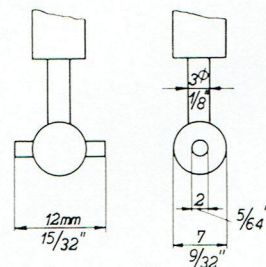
Outil pour la manœuvre des boutons de réglage.
